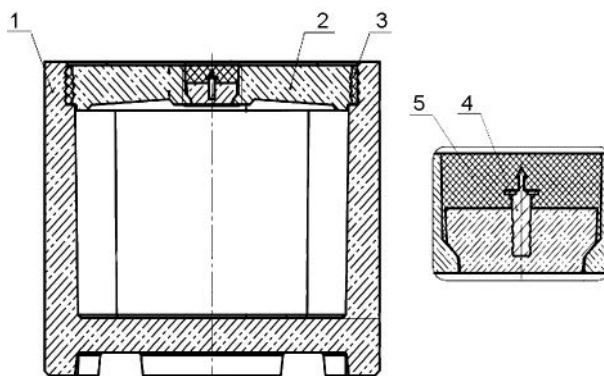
Общий вид контейнера (вид в разрезе): 1 – корпус контейнера; 2 – крышка; 3 – герметизирующая смесь; 4 – пробка; 5 – герметизирующая смесь пробки
